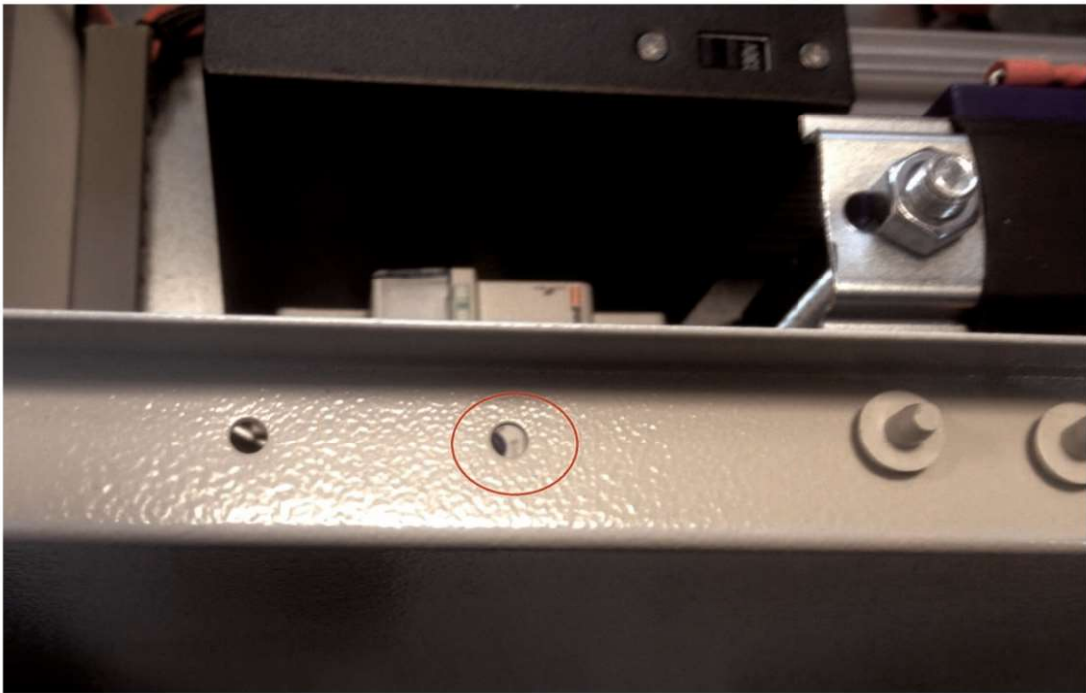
Резиновые заглушки вынуты из отверстий.
